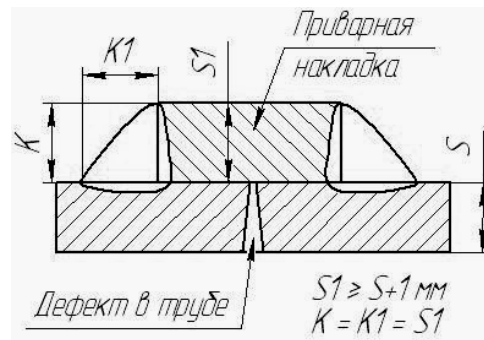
Конструкция нахлесточного сварного соединения при ремонте методом приварной накладки.
